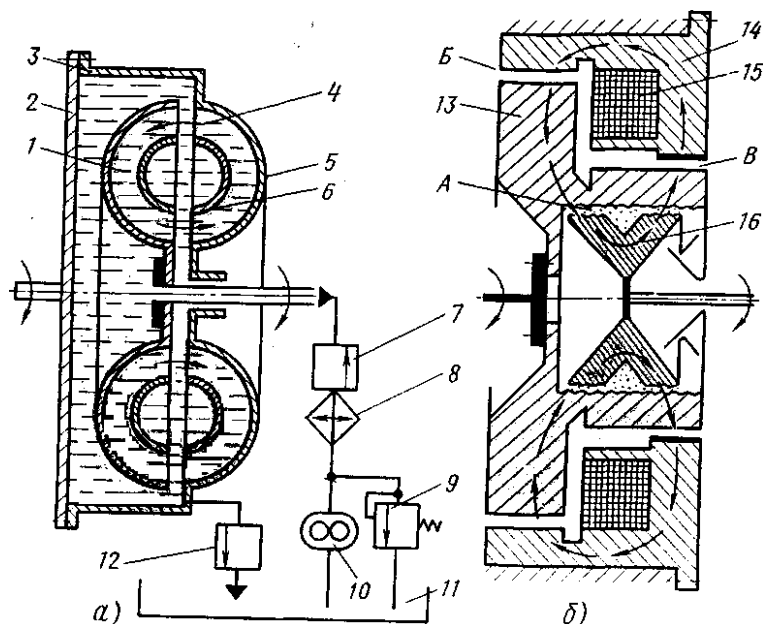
Схемы сцеплений: а - гидравлическую; б — электромагнитного порошкового
